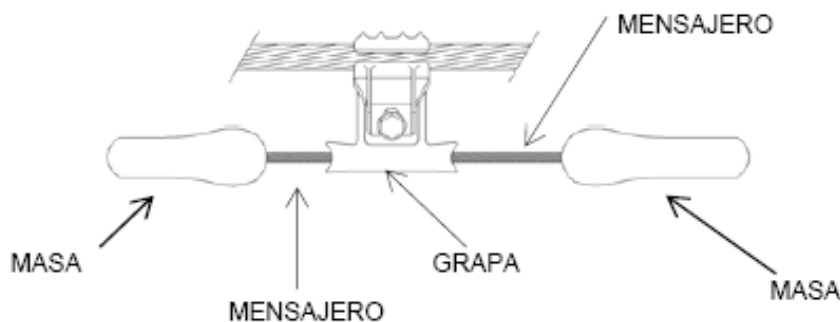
Instalación de amortiguador tipo Stock bridge
